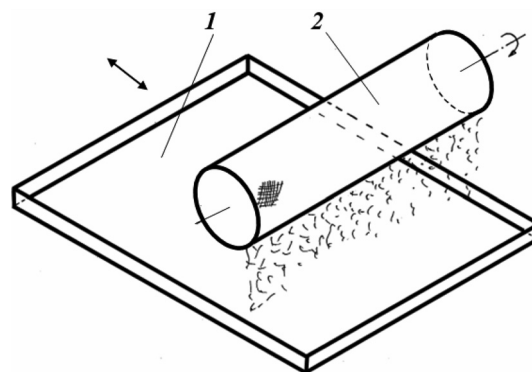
Схема процесса воздушного войлокования листового материала: 1 – подложка; 2 – вращающийся трубчатый сетчатый дозатор
